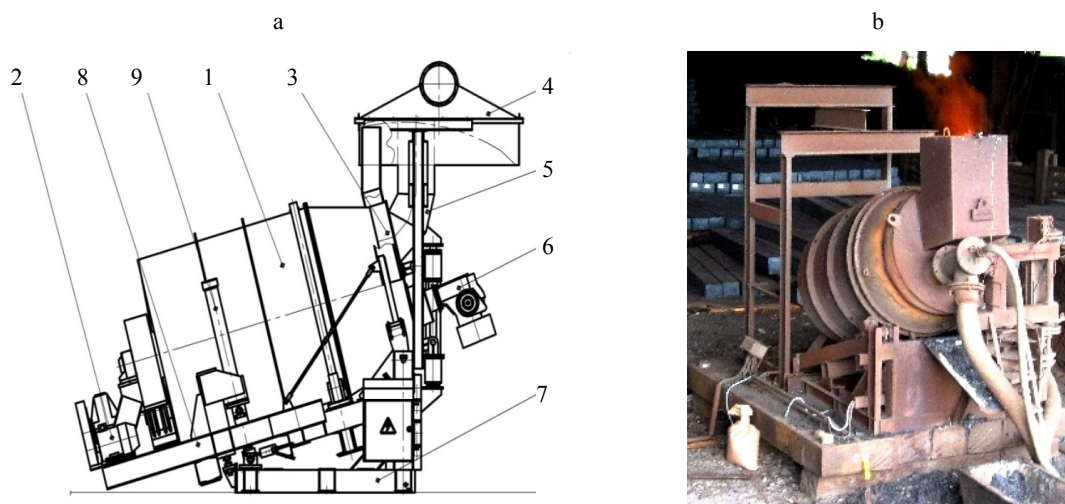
Ротационная наклоняющаяся печь: 1 – корпус печи; 2 – привод вращения; 3 – поворотная крышка; 4 – зонт; 5 – дымоход; 6 – горелка; 7 – опорная рама; 8 – поворотная рама; 9 – привод наклона печи; а – общий вид РНП емкостью 1,5 т; б – опытно-экспериментальная РНП емкостью 0,5 т
